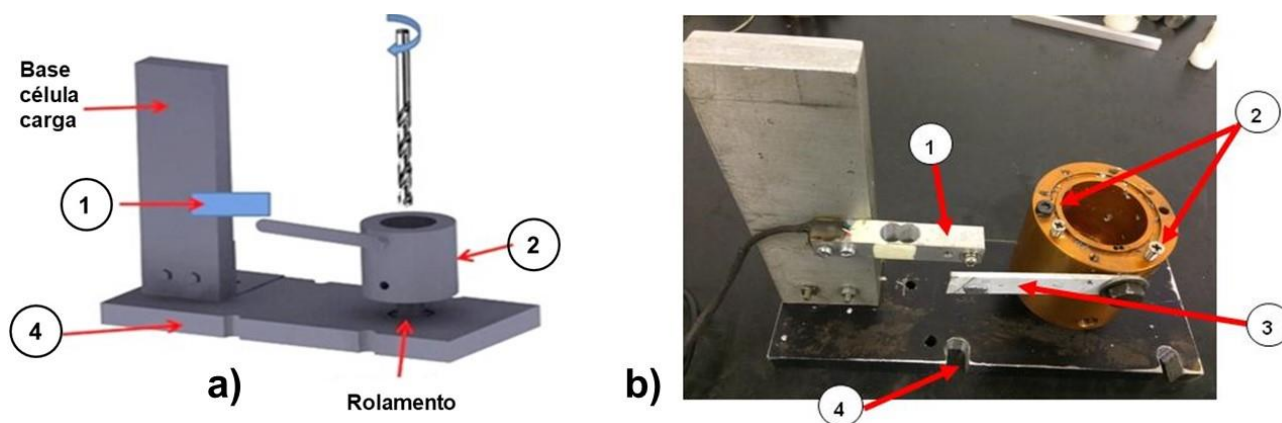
a) Projeto em 3D do dispositivo e b) arranjo final real
